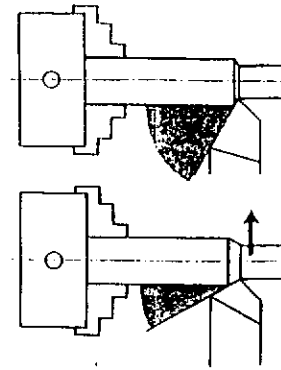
Un pequeño ángulo de posición da lugar a flexión.
